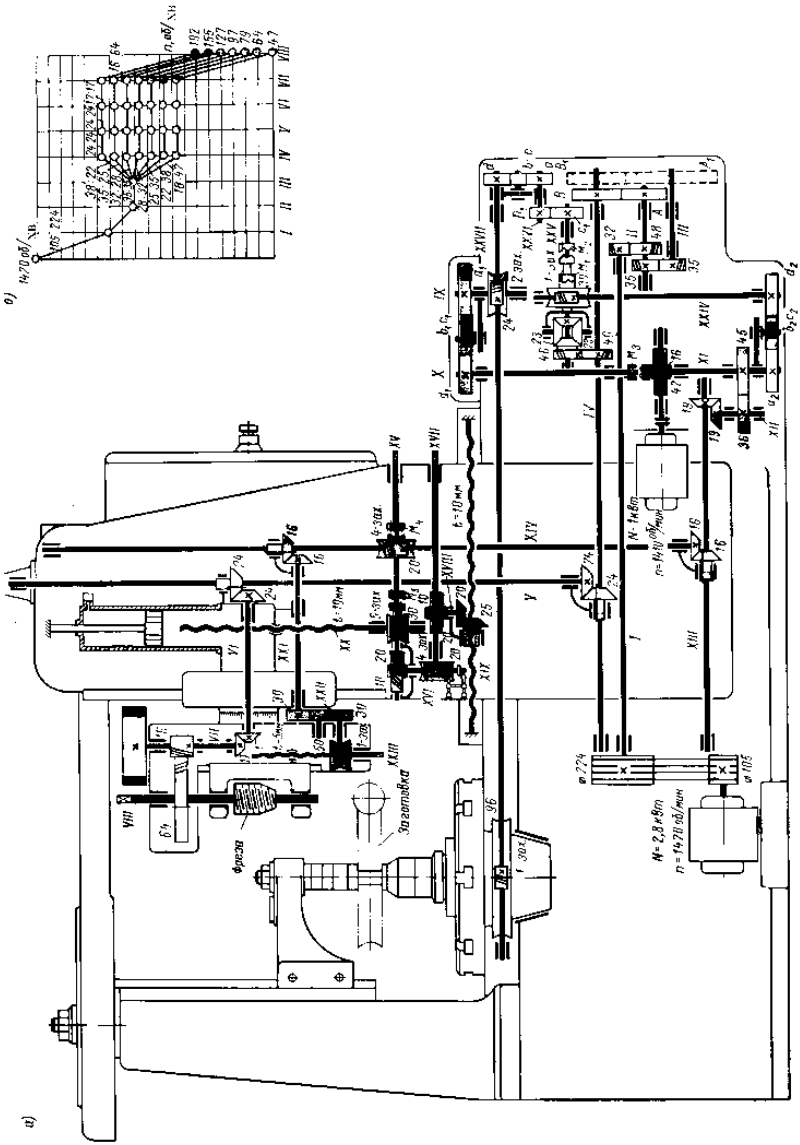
Кінематична схема зубофрезерного верстата мод. 5Д32
